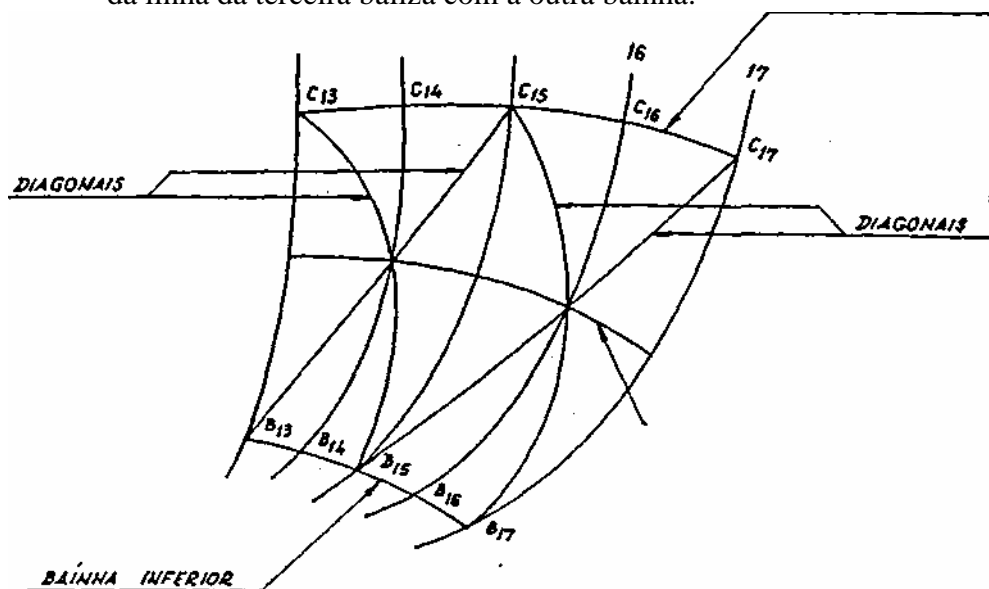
PLANO VERTICAL: Chapa da zona de ré
